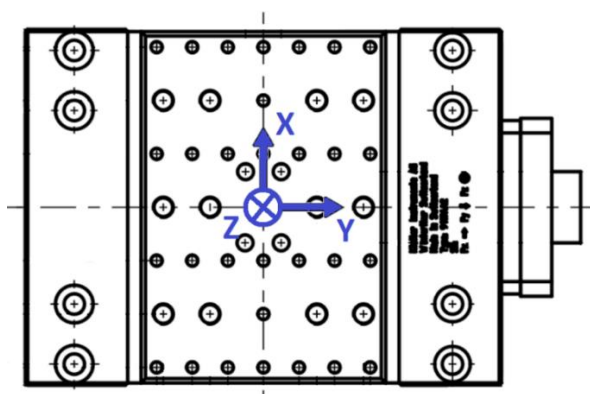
Dynamometr Kistler typ 9119AA2 [62].
